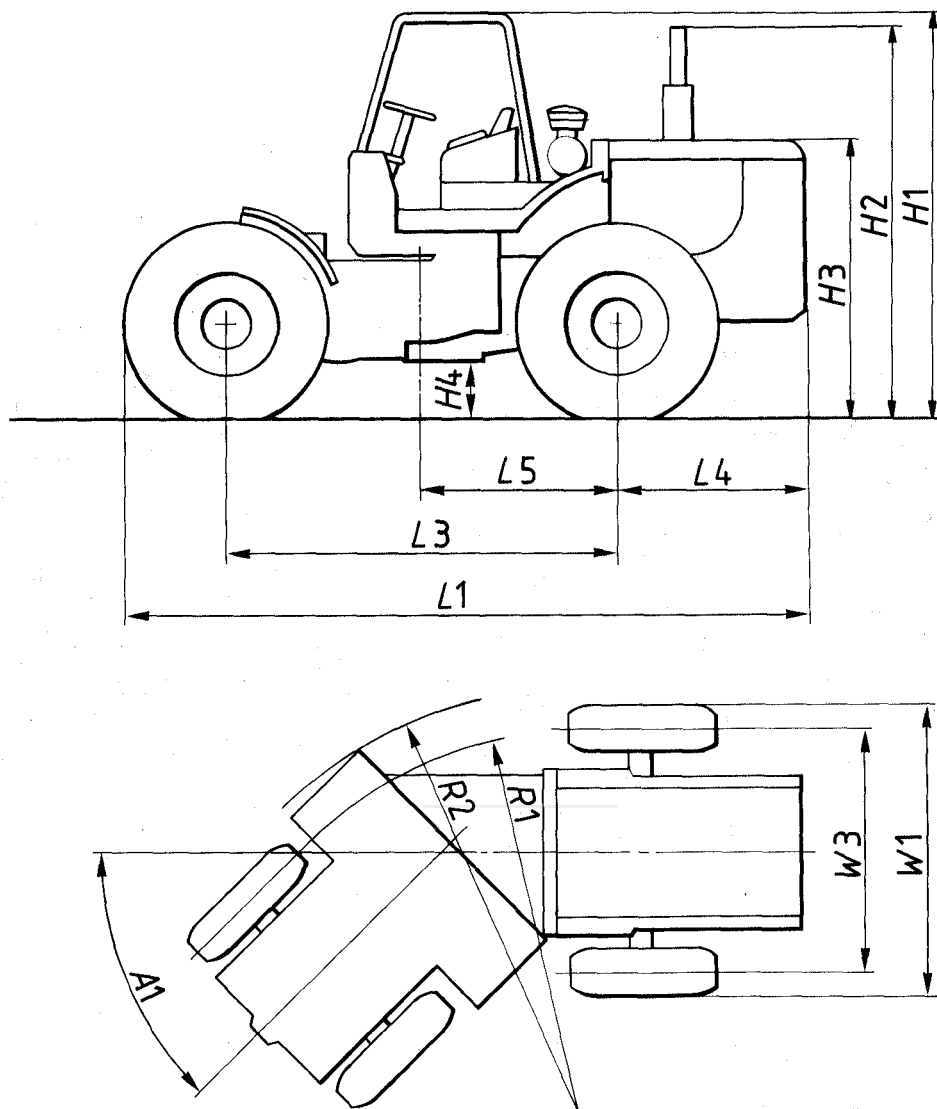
Dimensions de l'engin de base (tracteur sur roues)
